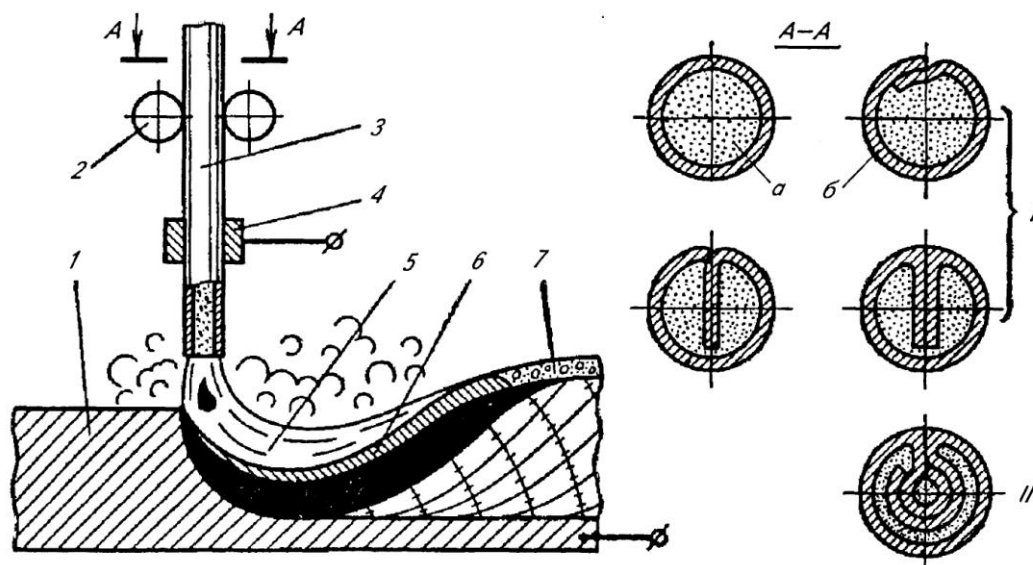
Схема электродуговой наплавки самозащитной порошковой проволокой:
